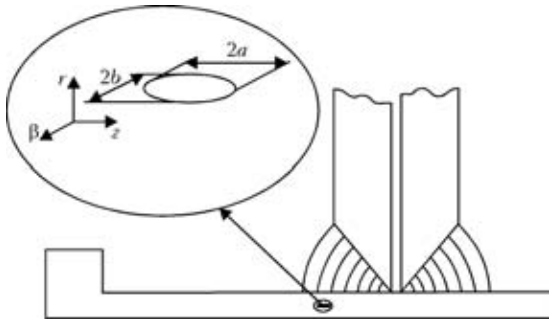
Схема ламелярной трещины в зоне сварного соединения: a, b — габаритные размеры ламелярной трещины
